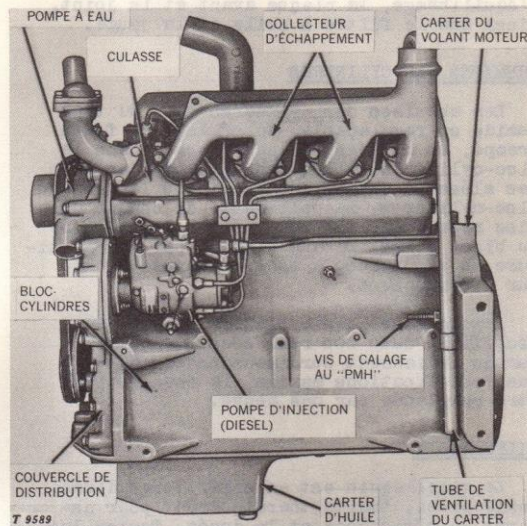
Vue du côté gauche du moteur Diesel
